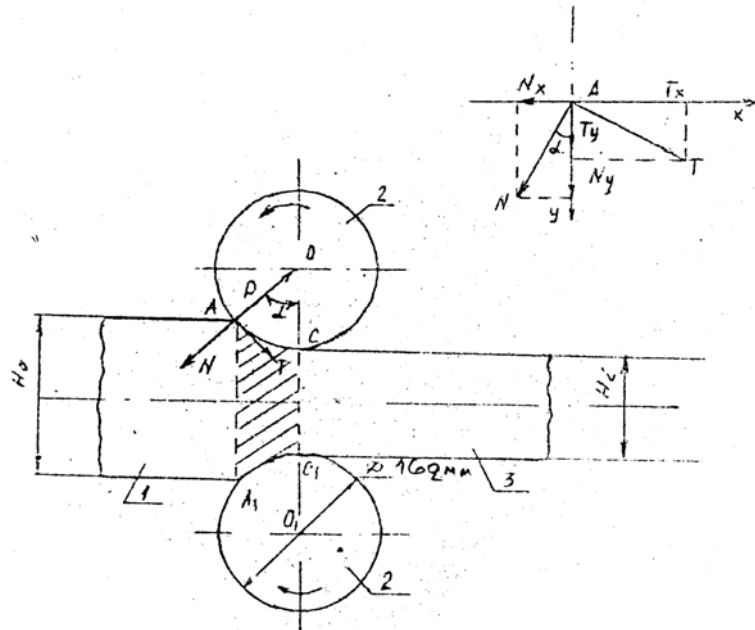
Схема подовжнього плющення: 1 - вихідна заготовка; 2 - робочі валяння; 3 - отримувана заготовка (прокат)
